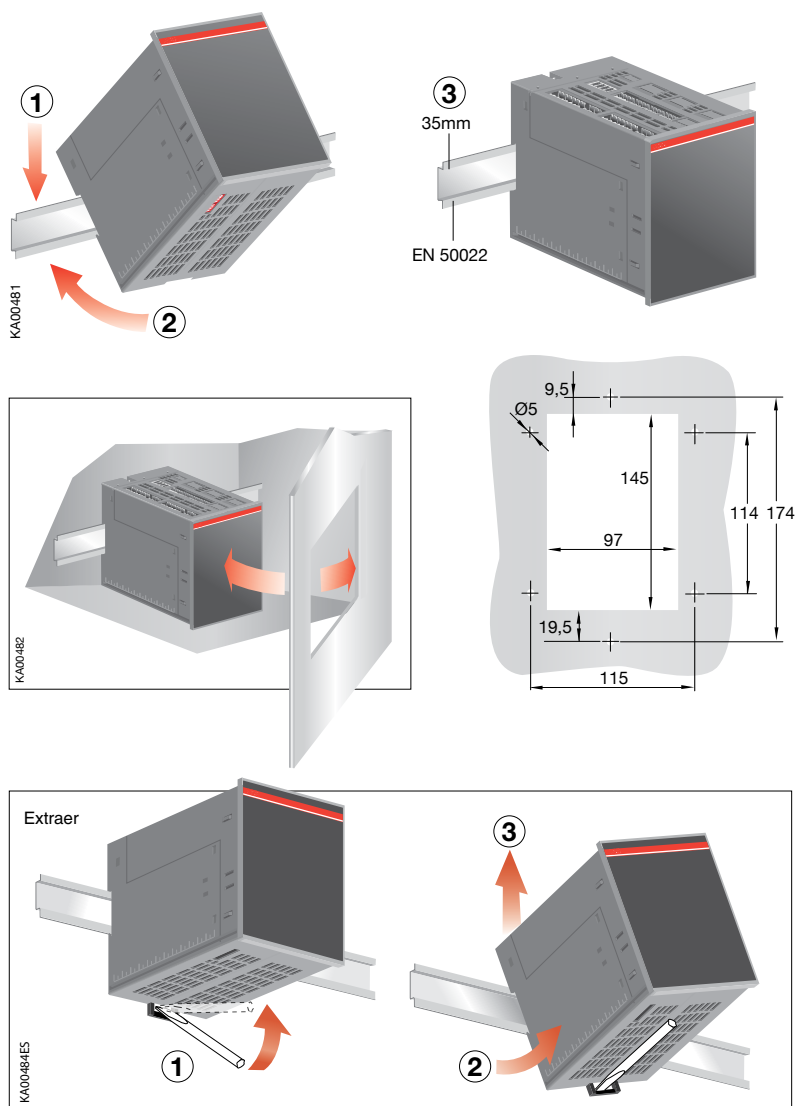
Dispositivo de conmutación automática ATS021, montaje sobre guía DIN
